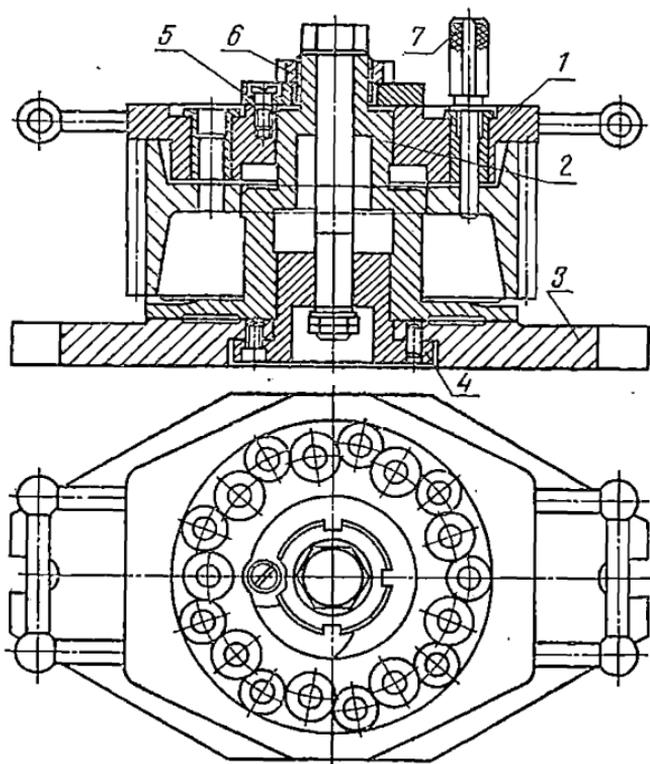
Накладной кондуктор для сверления отверстий в зубчатом колесе:
